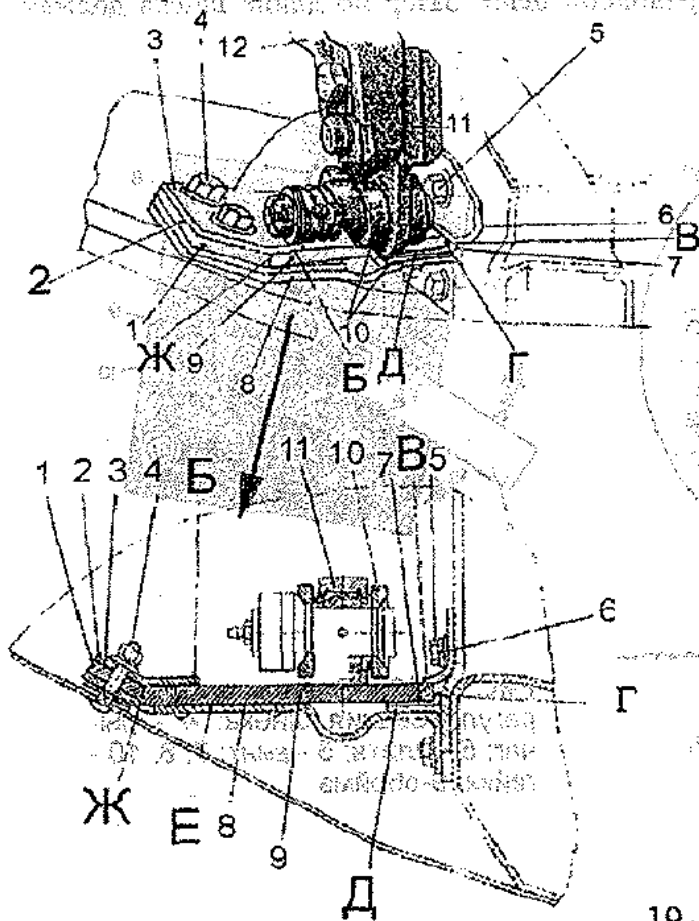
Схема соединения ножа с приводом: 1, 7-пластины трения; 2-регулирующая прокладка; 3, 6 - прижимы; 4, 5-болты; 8-пластина; 9-голка ножа; 10-щетка; 11-головка рычага; 12-рычаг; Б, В, Г, Д, Е и Ж – места контроля зазоров
